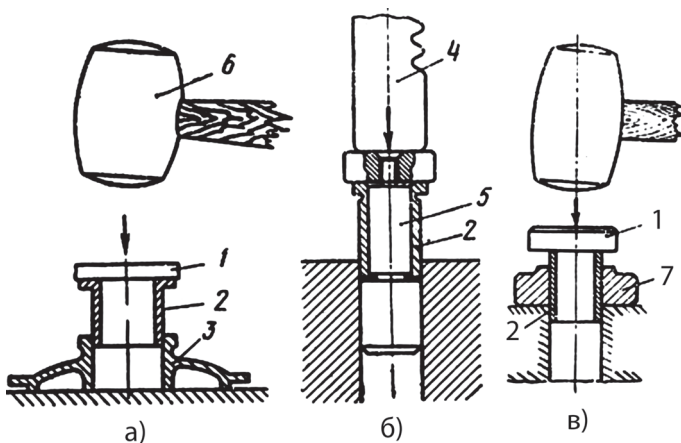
Запрессовка втулок в корпус подшипника:
